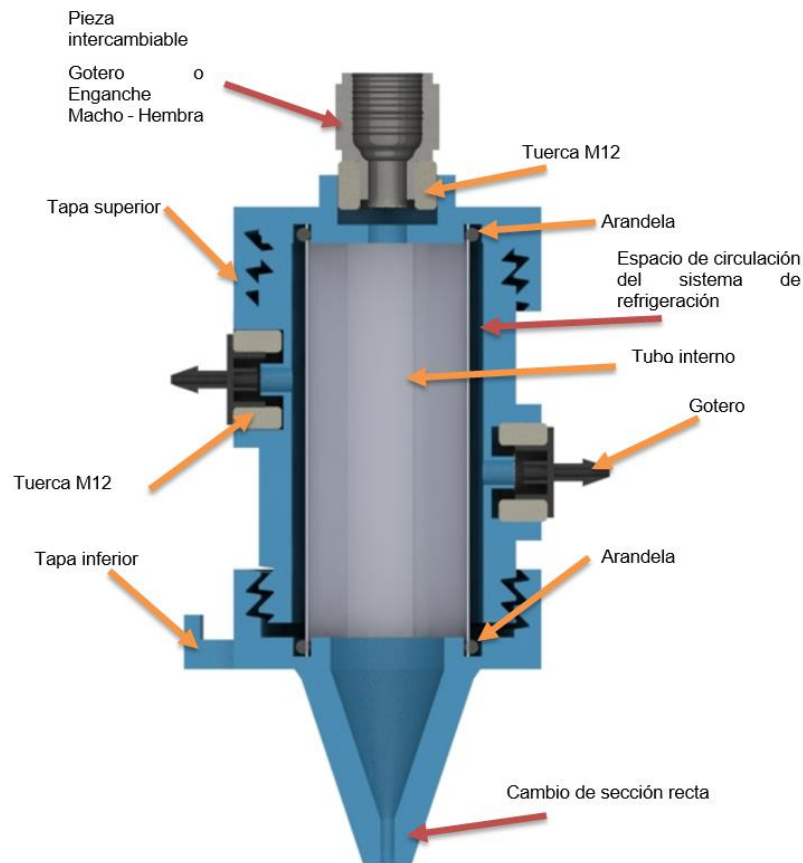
Ensamblaje del extrusor con la pieza enganche Macho - Hembra
